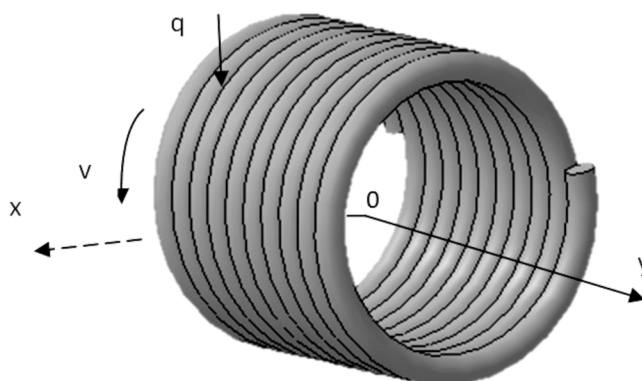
Схема лазерной сварки витков пружинно-витого канала
